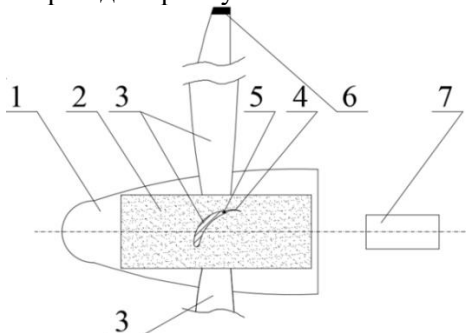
Лопатевий апарат вітрогенераторної установки: 1 – маточина; 2 – механізм зміну кута атаки лопаті; 3 – лопать; 4 – закрилок; 5 – п'єзоелектричний привід закрилки; 6 – азимутальний датчик вітру; 7 – центральний процесор установки
